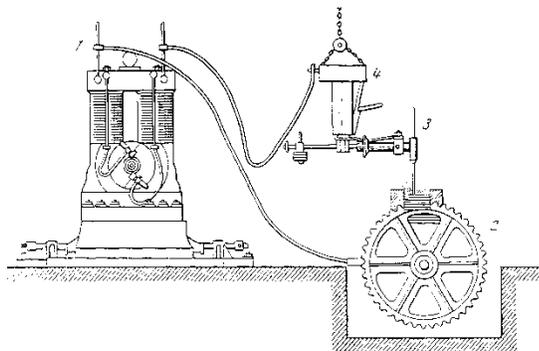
Сварочный аппарат Славянова Николая Гавриловича
